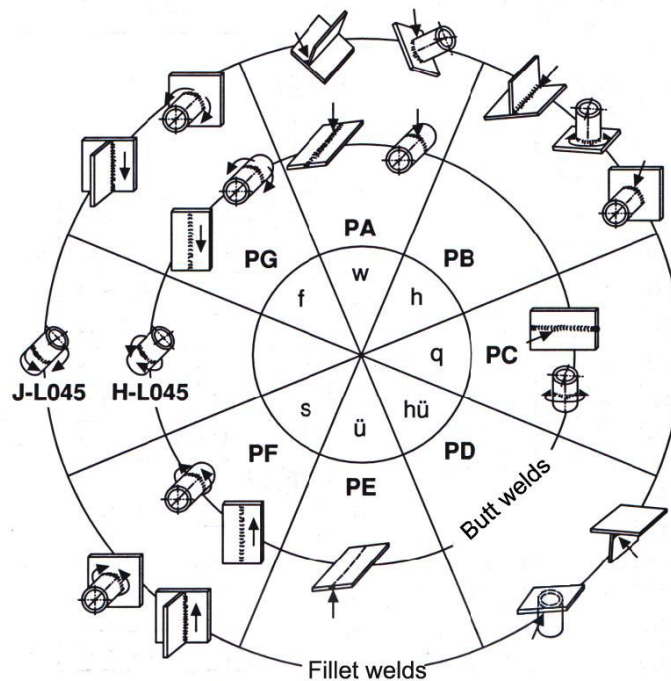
Posições de exame de qualificação de soldadores e procedimentos de soldadura [91]
